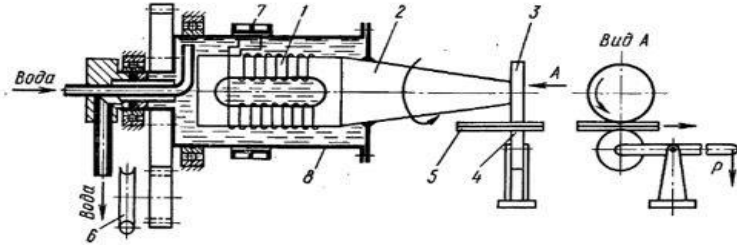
Схема установки для роликовой (шовной) сварки ультразвуком состоит из [5]: 1 – электромеханического преобразователя; 2 – трансформатора упругих колебаний; 3 – сваривающего ролика; 4 – прижимного ролика; 5 – изделия; 6 – механизма привода; 7 – подвода тока от ультразвукового генератора; 8 – кожа преобразователя.
